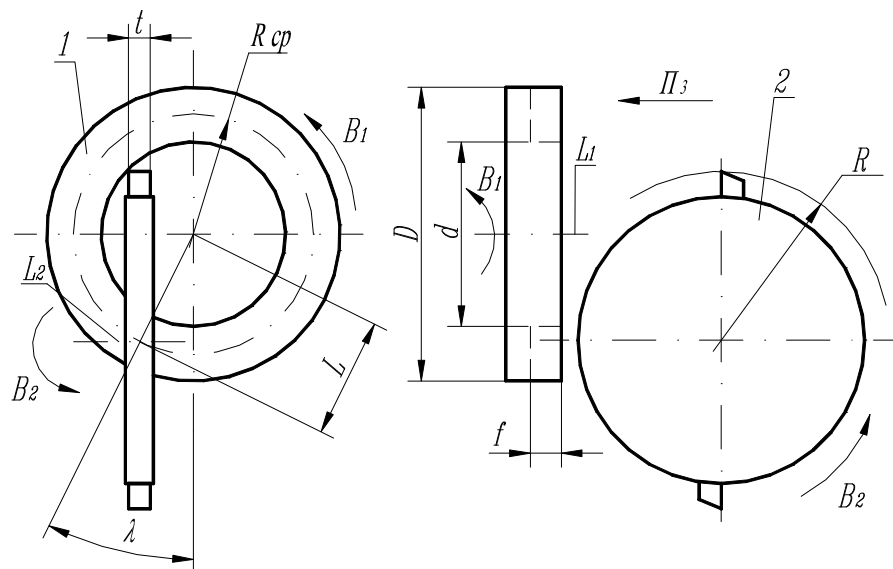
Схема обработки торцового зубчатого контура резцовой головкой
